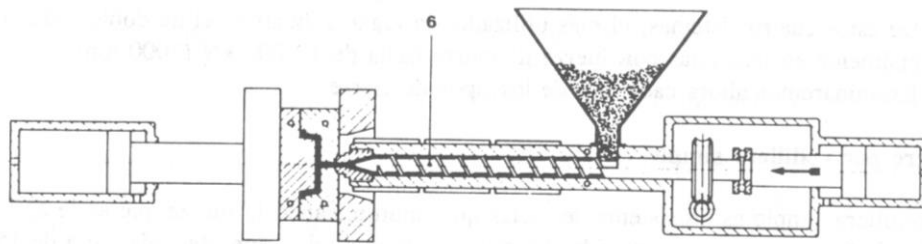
diagrama simplificado de una máquina de moldeo por inyección con husillo recíprocante. Nótese que el molde está cerrado, mientras que el husillo (6) está al final de la cámara de inyección.
